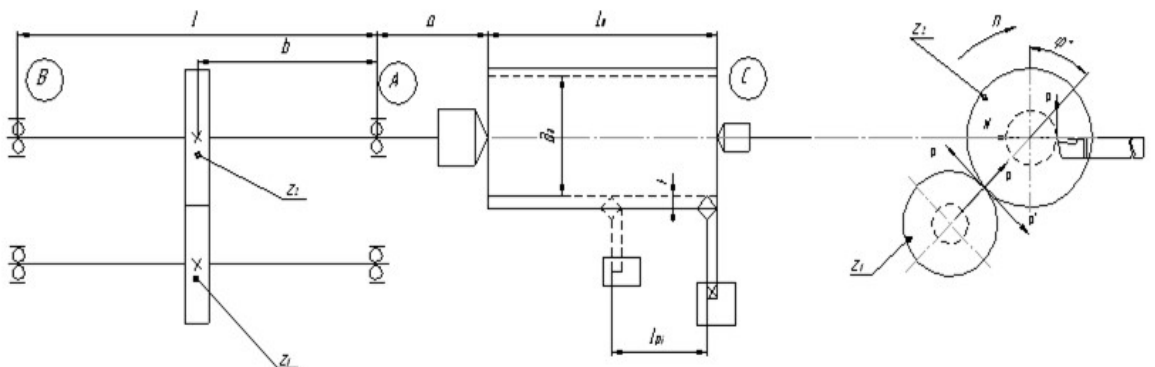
Розрахункова схема оброблення деталі на токарному верстаті з ЧПК
